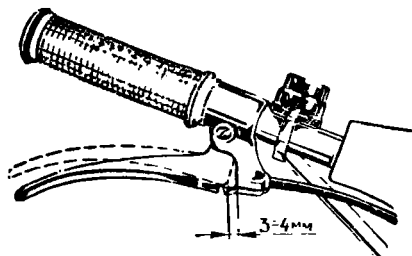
Свободный ход рычага переднего (ручного) тормоза.
